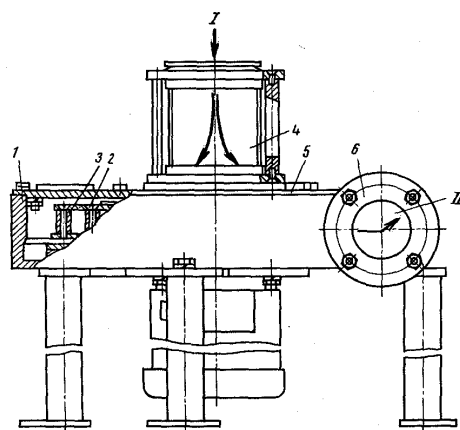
Схема ентолейтора РЗ-БЭР: 1 – корпус; 2 – диски; 3 – втулка; 4 – прийомний патрубок; 5 – кришка; 6 – випускний патрубок; I – вихідний продукт; II – роздрібнений продукт.
